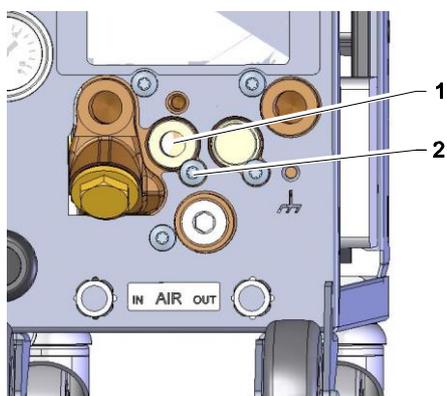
Ligação separada da entrada de água de refrigeração e do sistema
